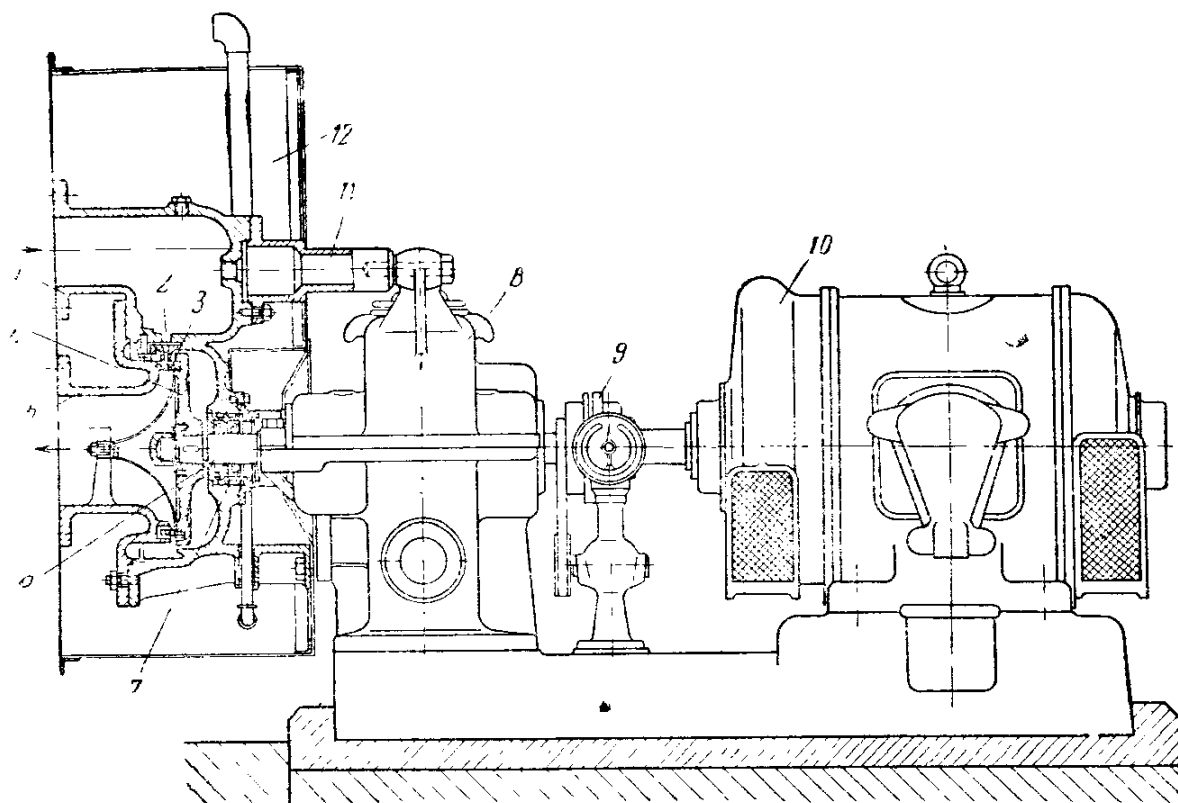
Общий вид турбодетандерного агрегата для кислородной установки типа КТ-3600:
